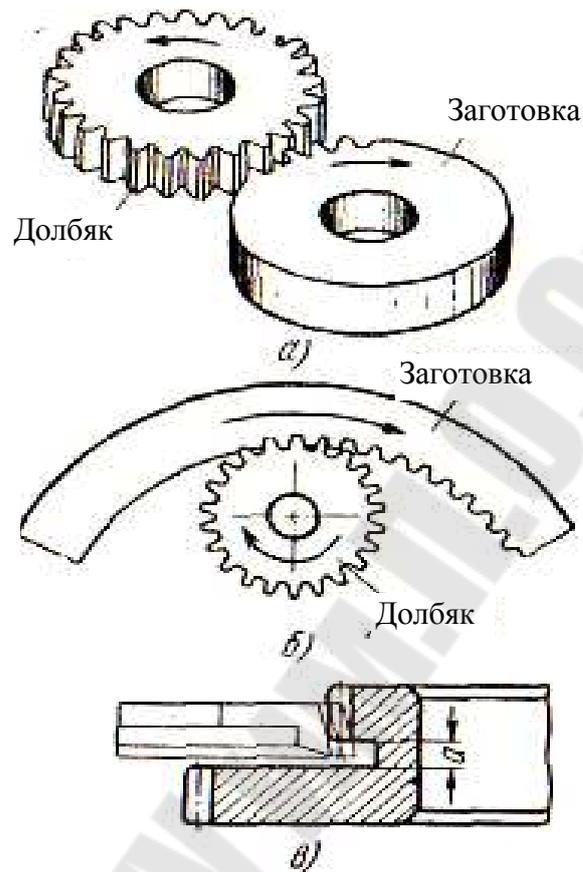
Схема нарезания зубьев колеса зуборезным долбяком
